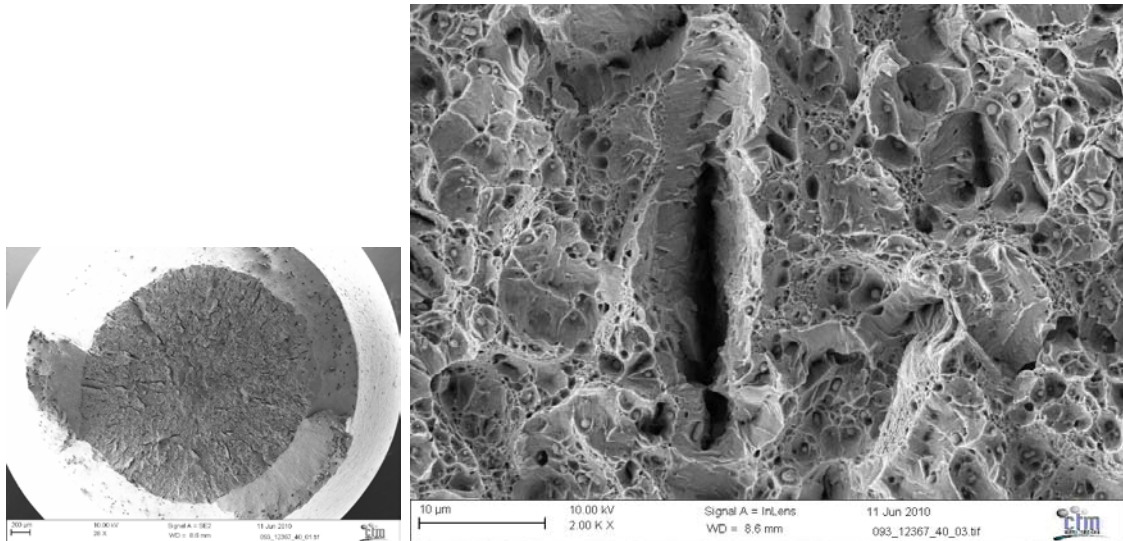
Superfície de fractura de la proveta de 1.2367 assajada en aire a 40°C.
